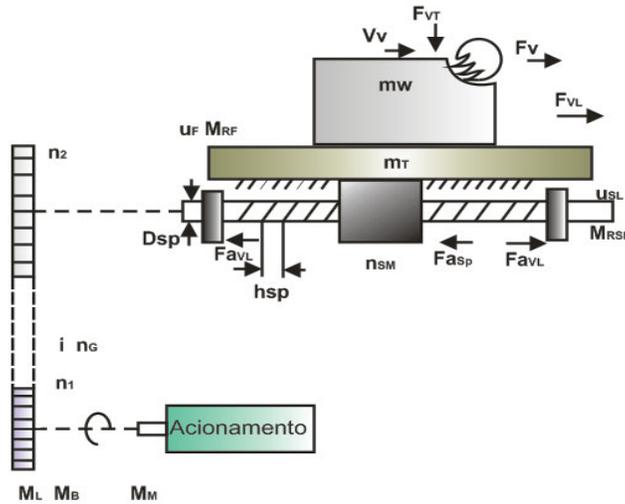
Desenho do eixo de uma máquina de usinagem com um sistema de transmissão conversora e transformadora
